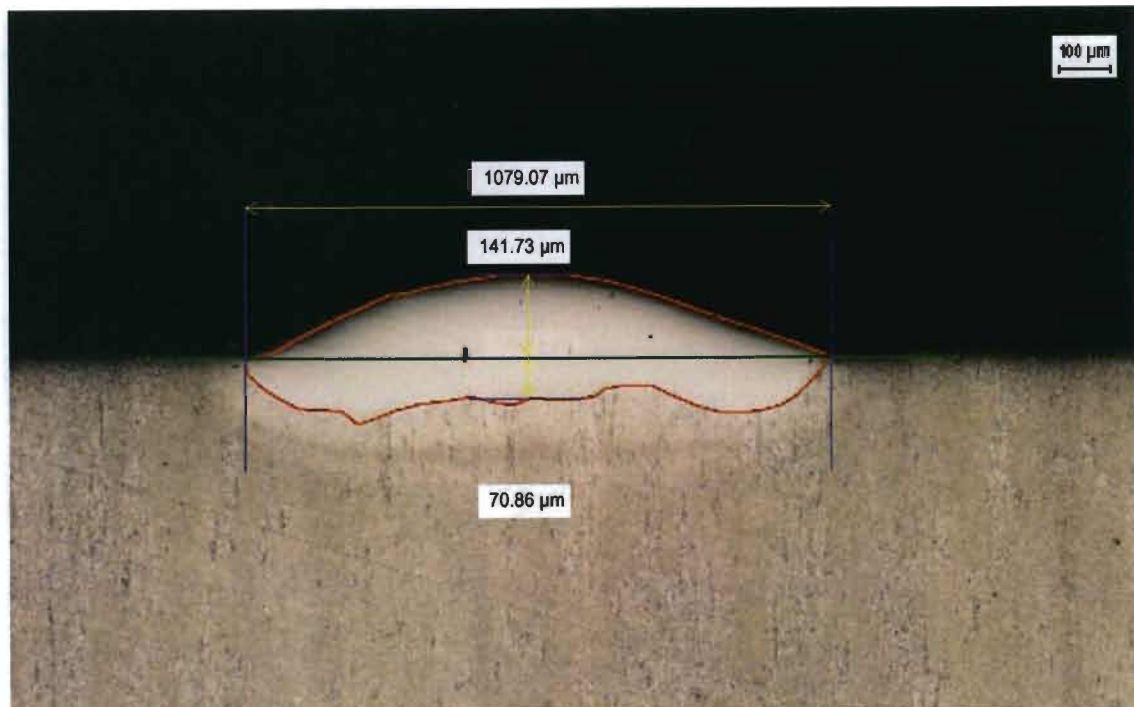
6 Cordón de soldadura 2 visto a 5X
